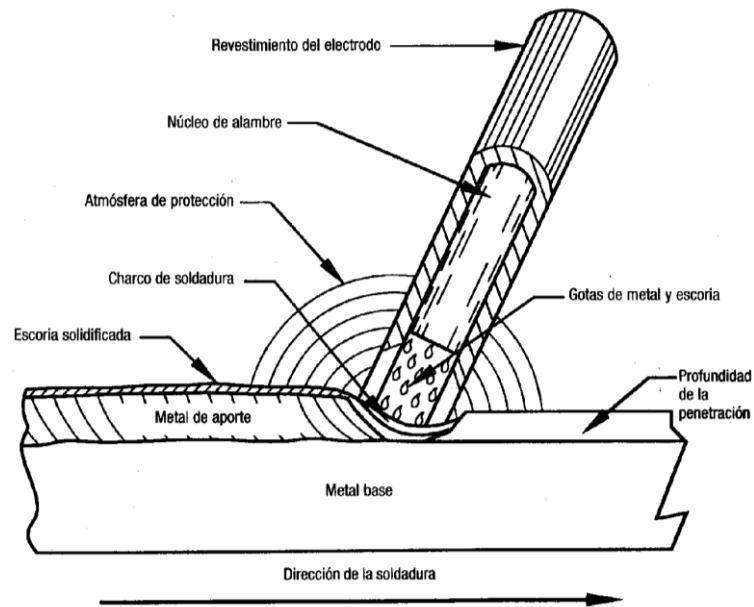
Proceso de Soldadura de Arco Metálico con electrodo revestido
